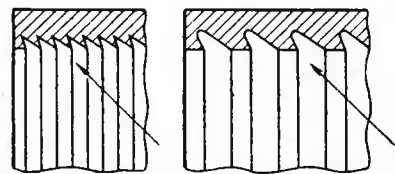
Схема подготовки внутренних поверхностей к металлизации
